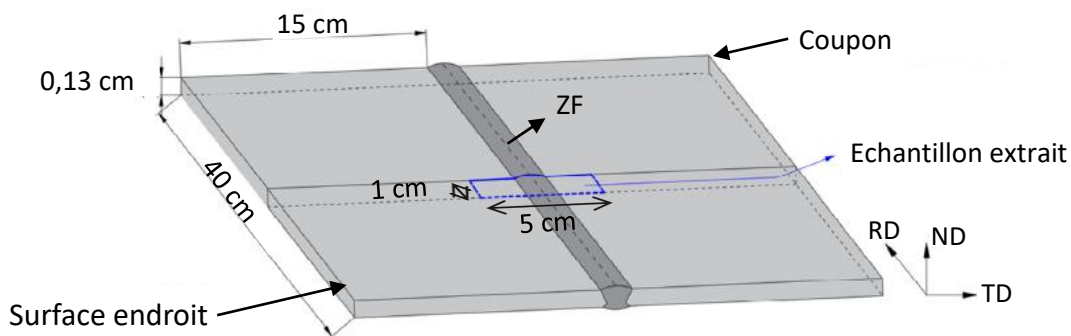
Echantillon extrait de la surface décapée de la soudure⁶¹. (TD : transversale direction, ND : normale direction et RD : direction de laminage)
